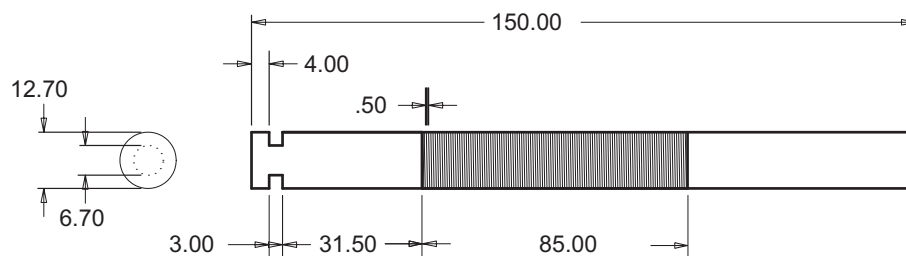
Tornillo sin fin. Dimensiones en mm.
